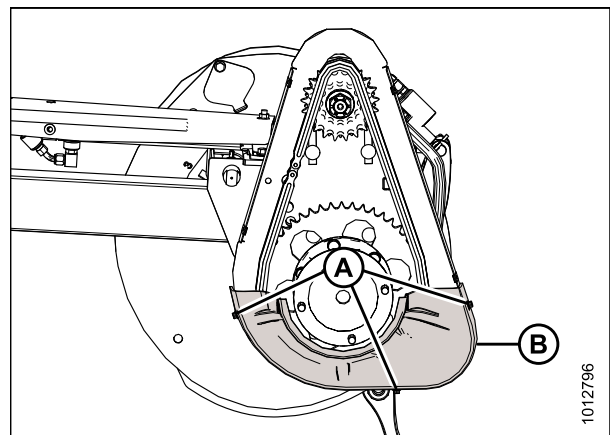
Tampa inferior da transmissão (tampa superior removida)
